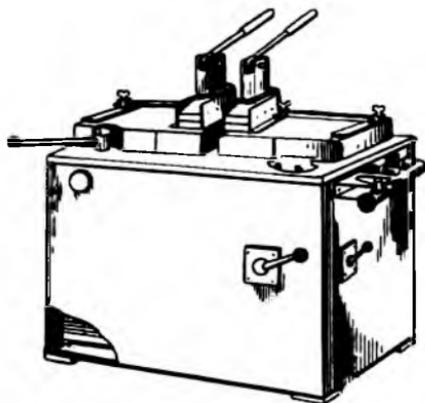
Электросварочный стыковой аппарат для стыковой сварки ленточных пил АСЛП-1
